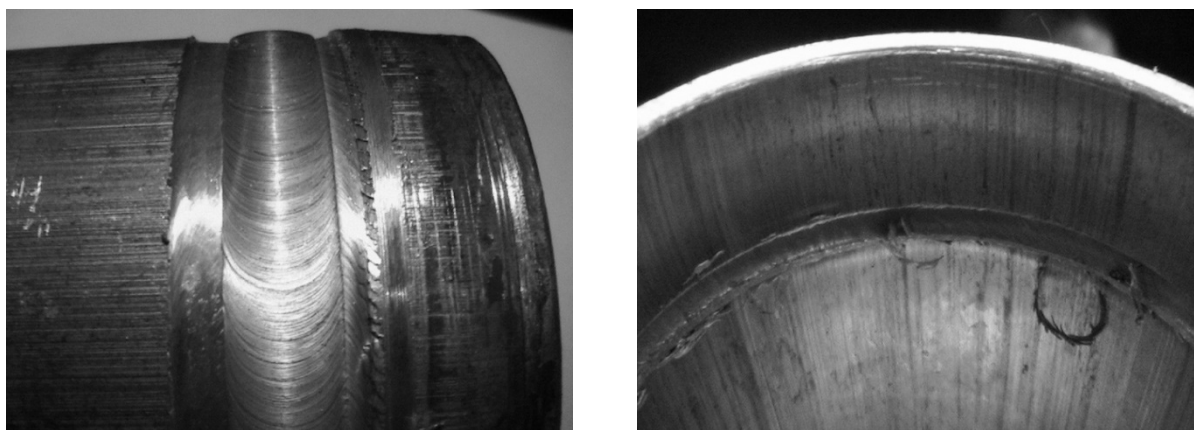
Сварочный шов снаружи (слева) и внутри (справа)
